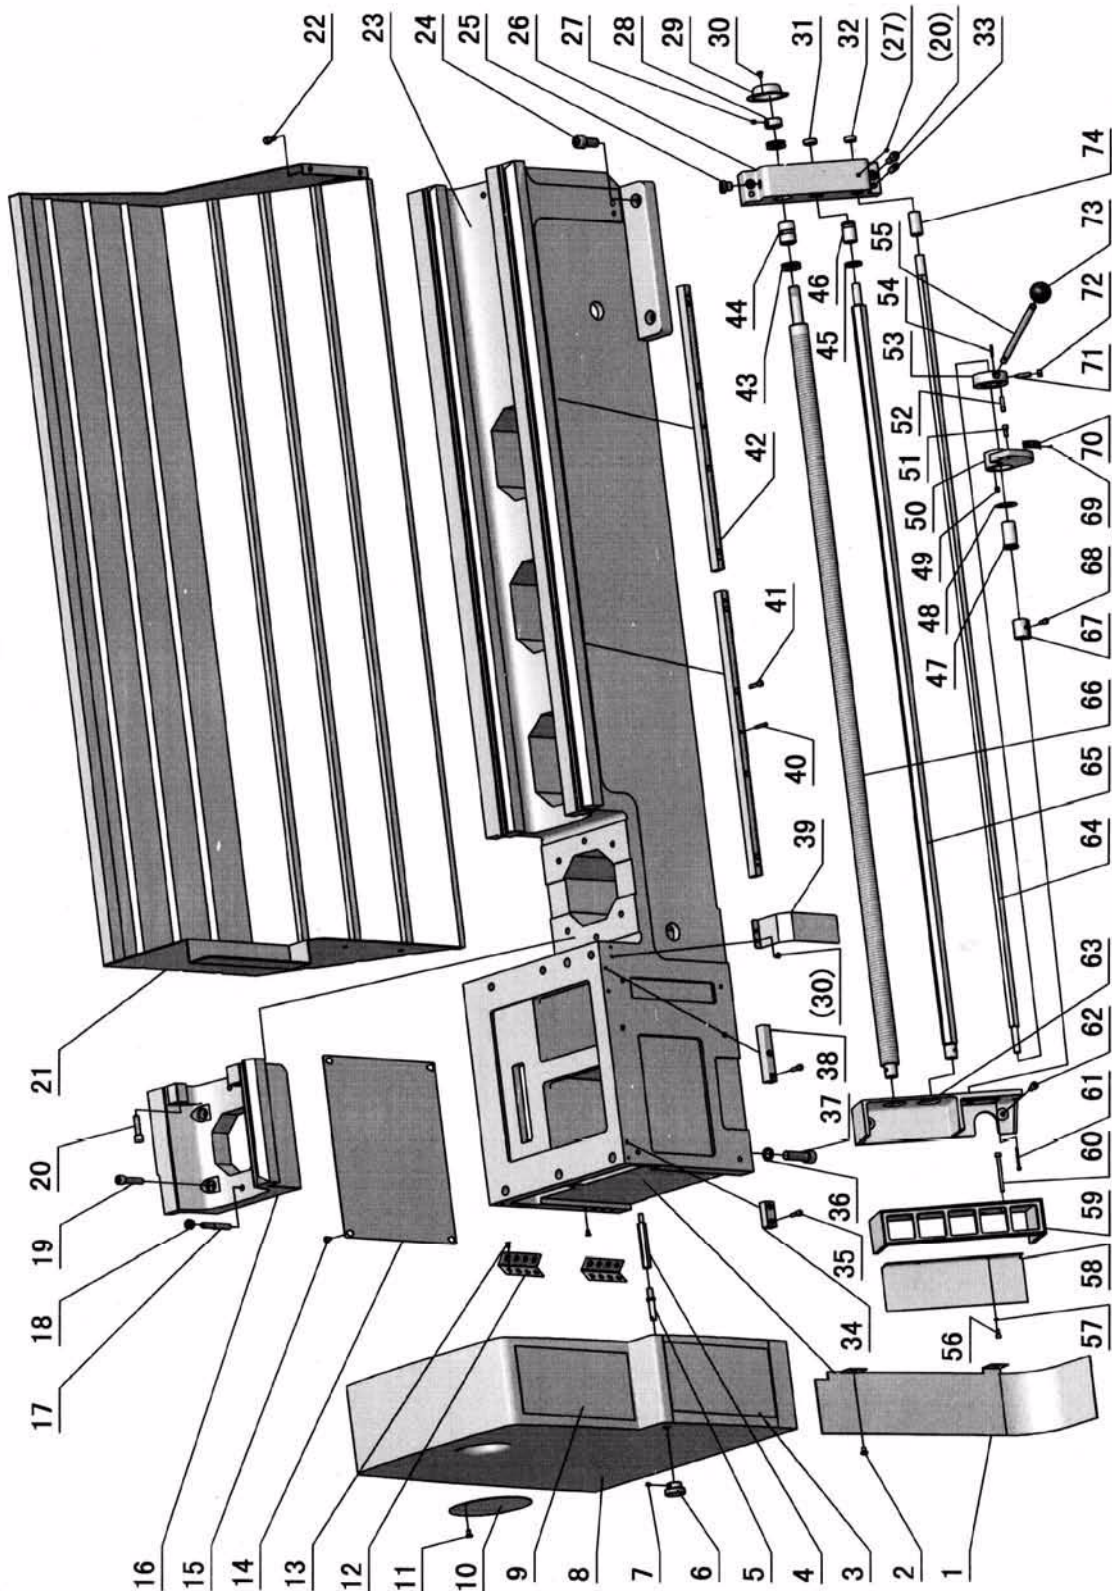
Maschinenbett, Vorschub, Abdeckungen - Machine bed, feed, covers
